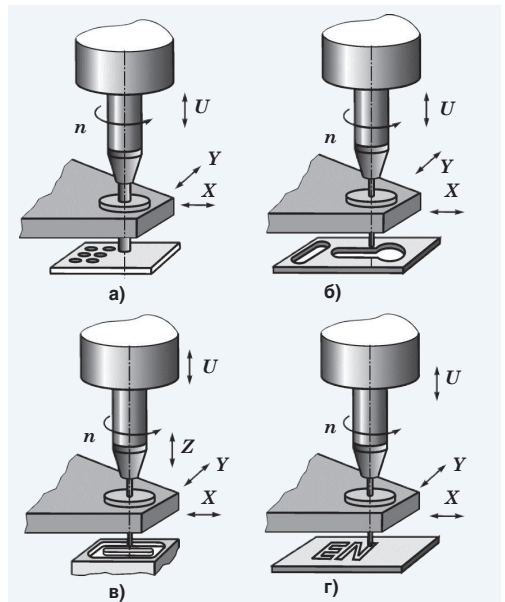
Схемы электроэрозионного фрезерования вращающимся стержневым или трубчатым ЭИ: а) обработка отверстий; б) вырезка из листового материала; в) обработка фасонных поверхностей; г) гравирование и маркирование
